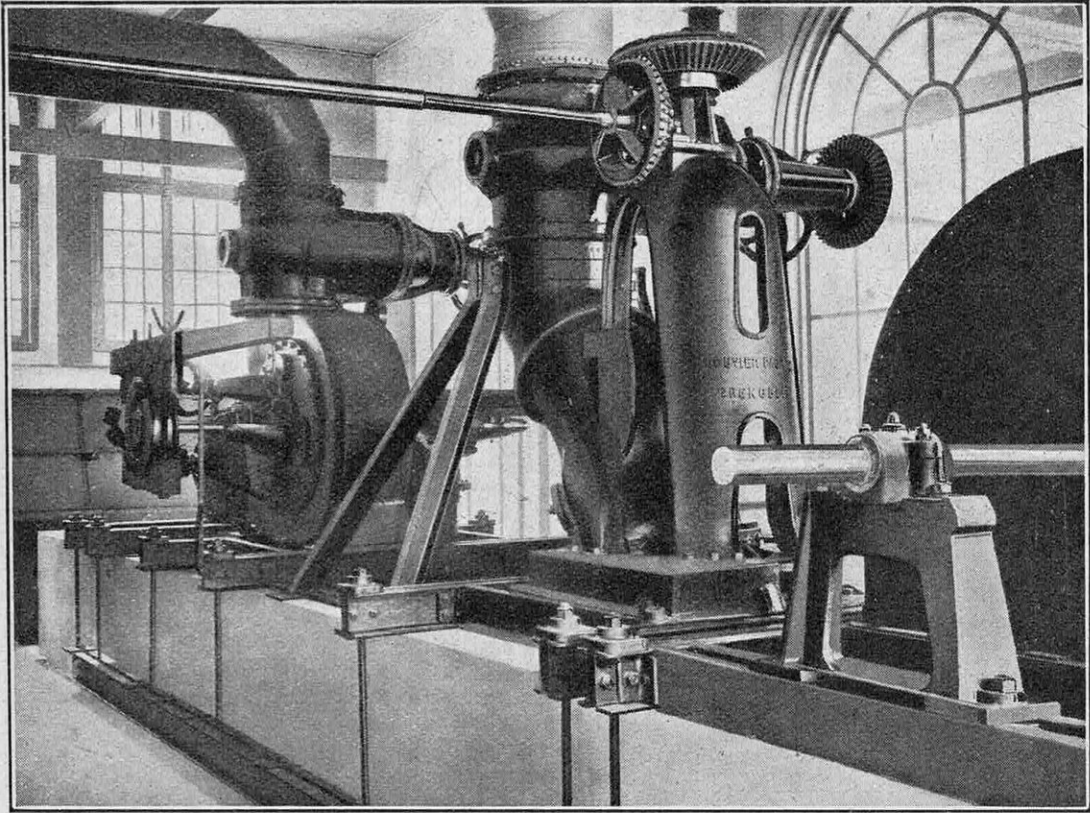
VUE PARTIELLE DE L'ATELIER DES MACHINES HYDRAULIQUES
